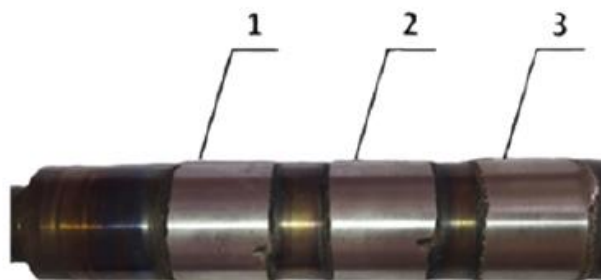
Наплавленный образец — вал $\varnothing 50$ из Ст40Х:
